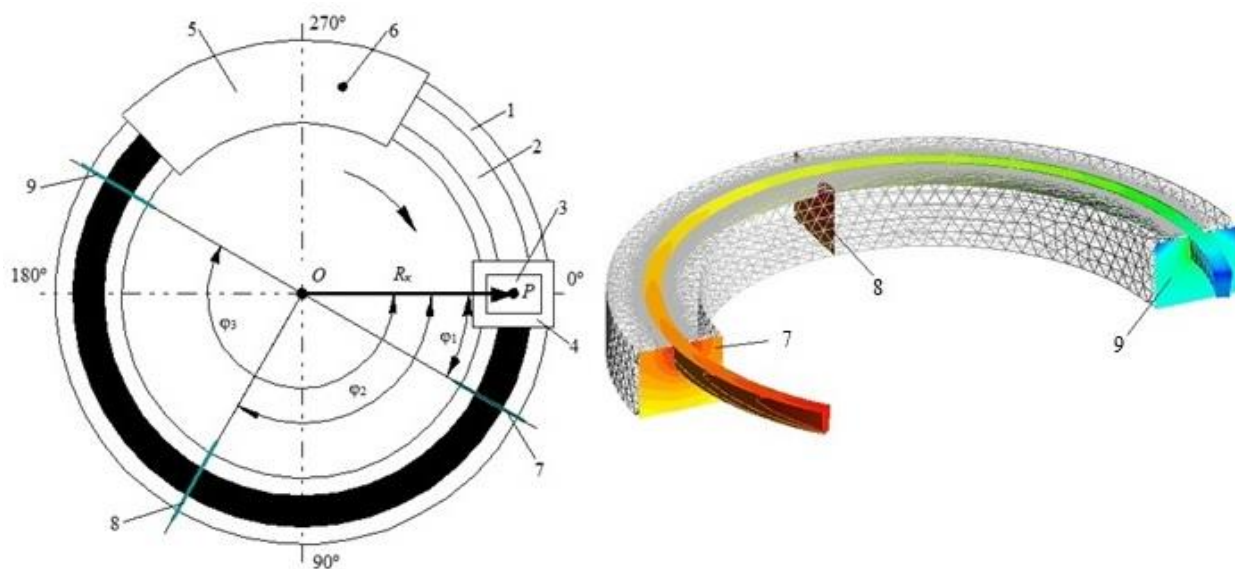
Схема установки непрерывного совмещенного литья и прессования с горизонтальным карусельным кристаллизатором:
